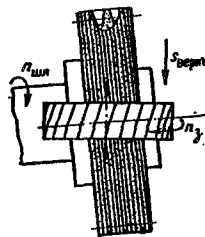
Схема шлифования зубьев цилиндрического колеса червячным кругом
